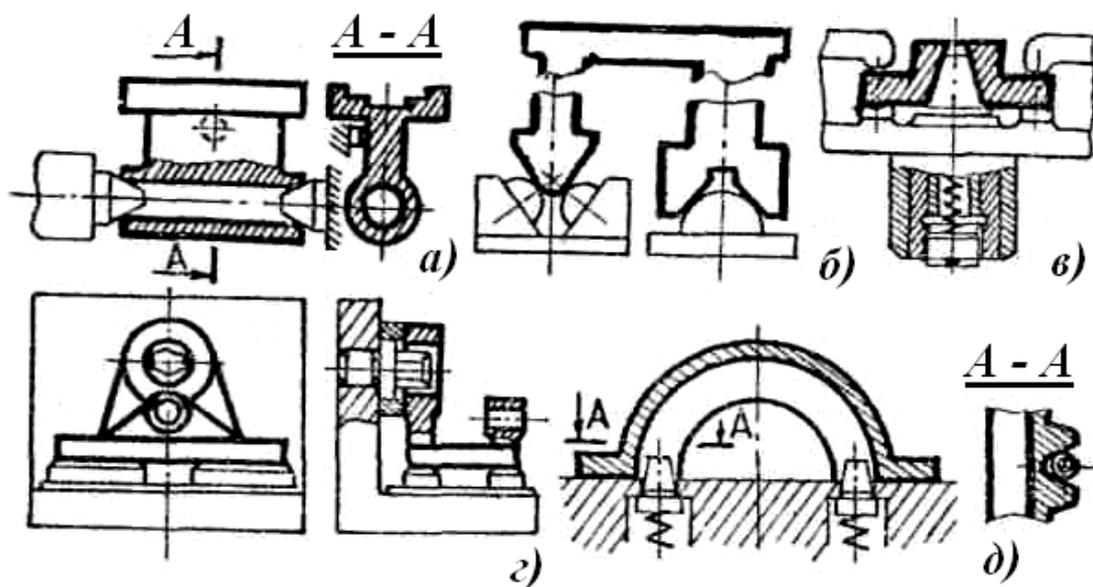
Комбинированные схемы установки корпусных деталей:
